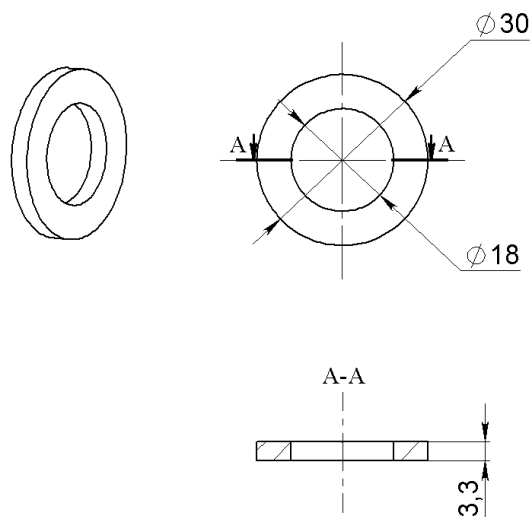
Типоразмеры пьезокерамического диска
